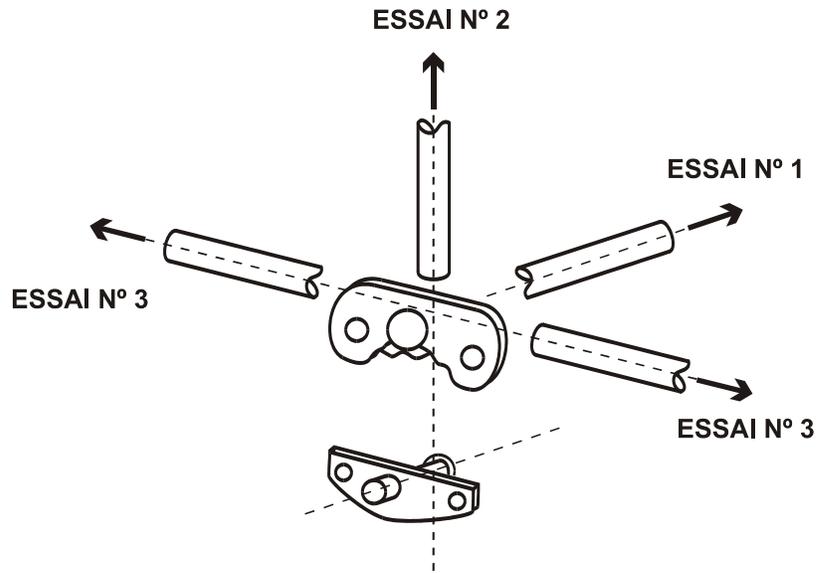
Montage pour l'essai d'application de la force numéro n° 1 sur le loquet de porte
